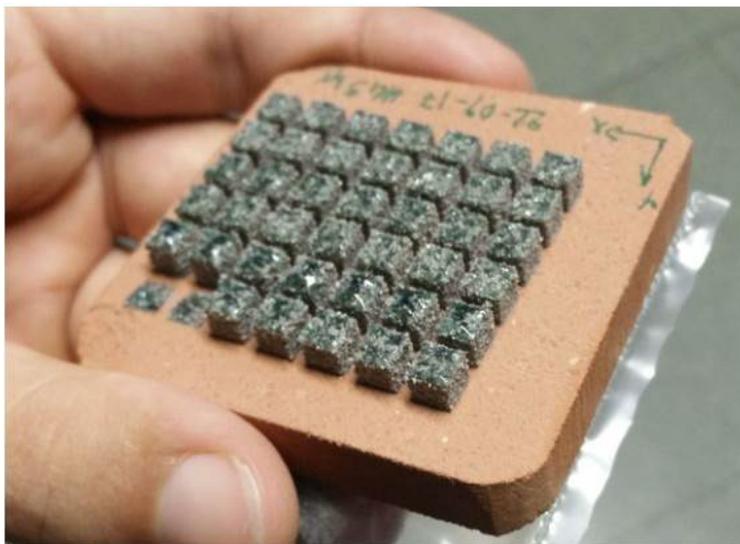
Образцы, изготовленные из лунного реголита [37].
